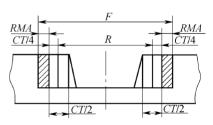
内对称加工表面铸件 基本尺寸示意图 R—铸件基本尺寸 F—零件尺寸 CT—铸件尺寸公差值
